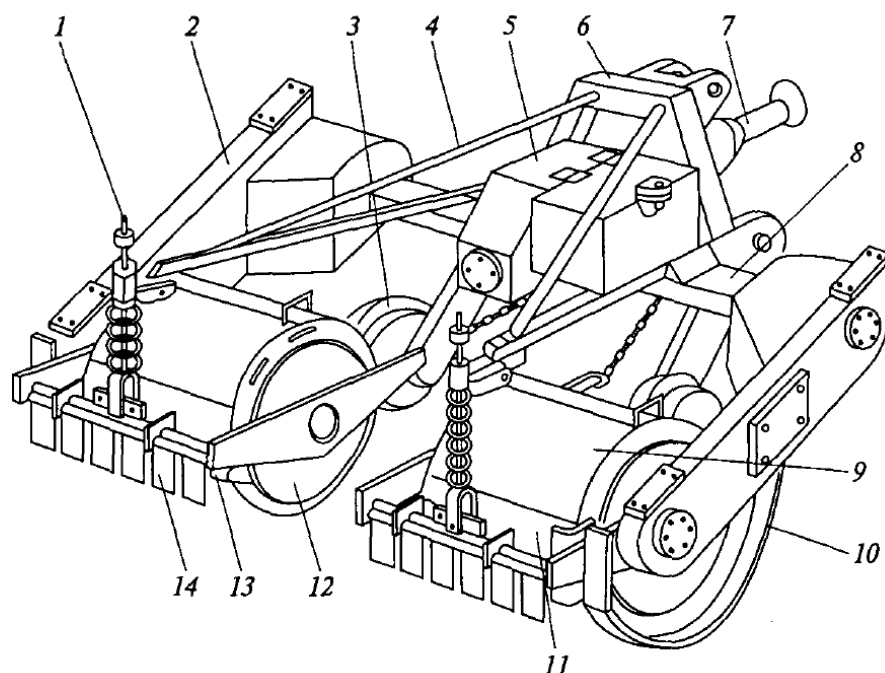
Культиватор фрезерный лесной КФЛ-1,4:
